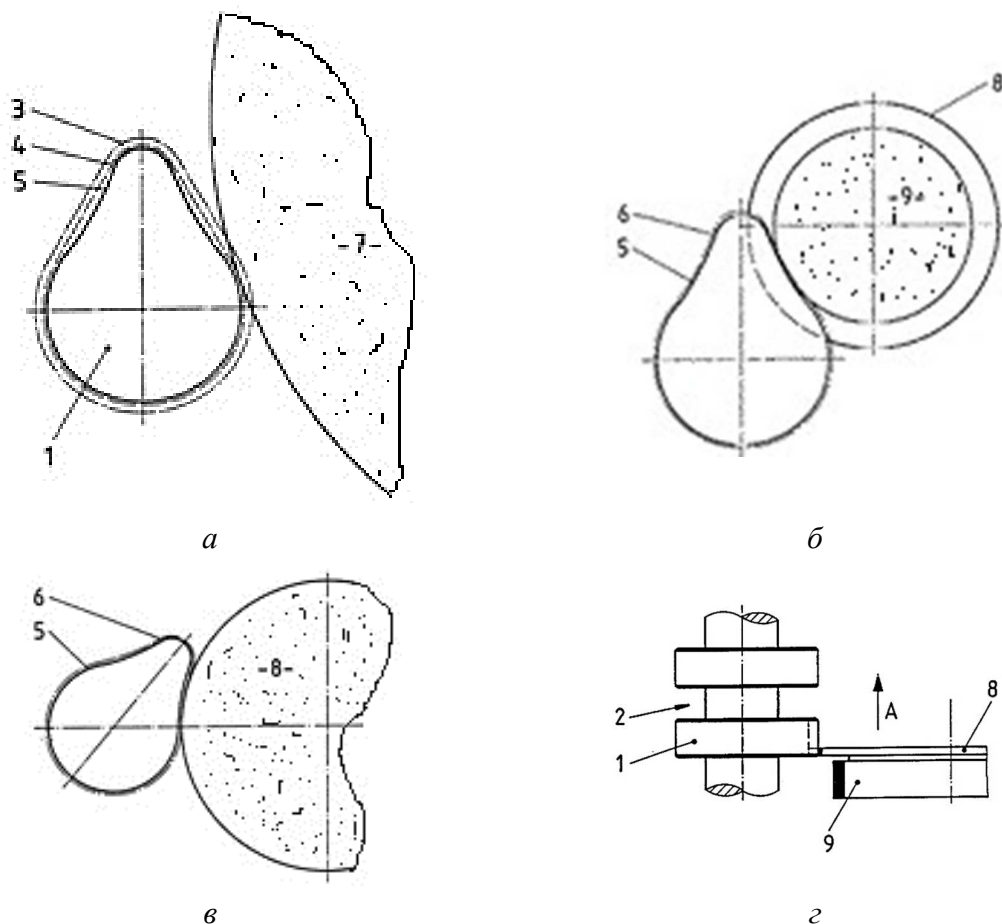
Схема обробки кулачка розподільного вала з увігнутими боковими поверхнями: а – вихідного 3 та проміжного 4 контуру кулачка; б – чистового шліфування кулачка; в, г – увігнутих бічних поверхонь на проміжному контурі кулачка; 1 – кулачок; 2 – розподільний вал; 3, 4, 6 – вихідний та проміжні контури кулачка; 5 – кінцевий контур кулачка; 7, 8, 9 – шліфувальні круги для чорнового та чистового шліфування
